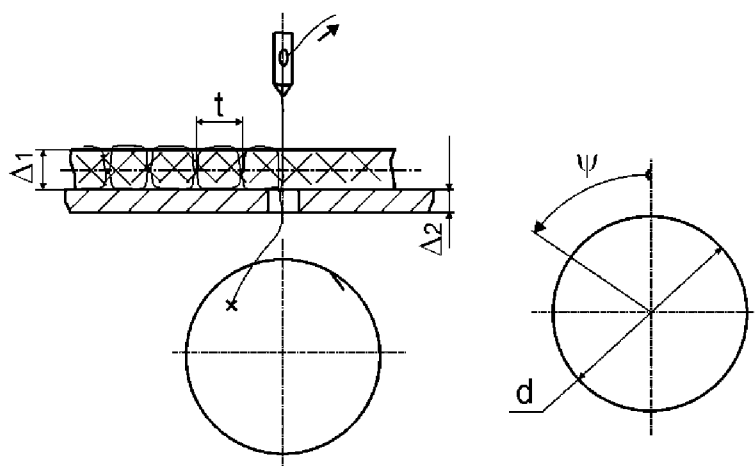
Схема затяжки стежка и угол поворота носика челнока
